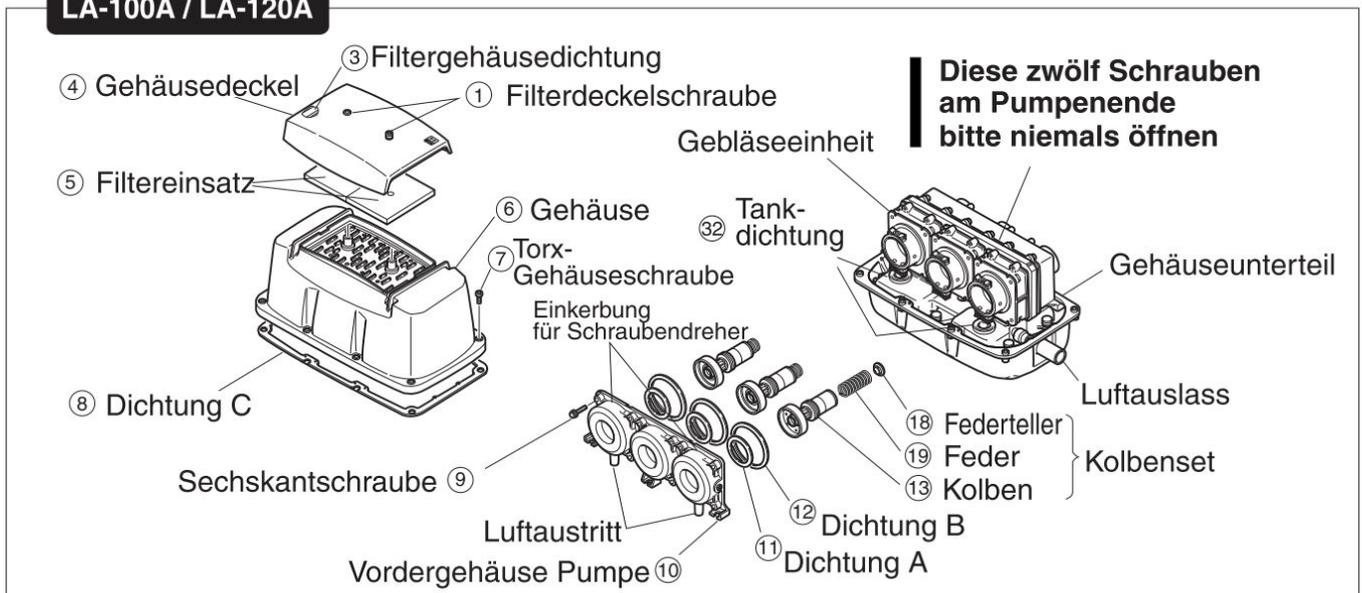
Explosionszeichnung Luftfilter Luftkompressor
